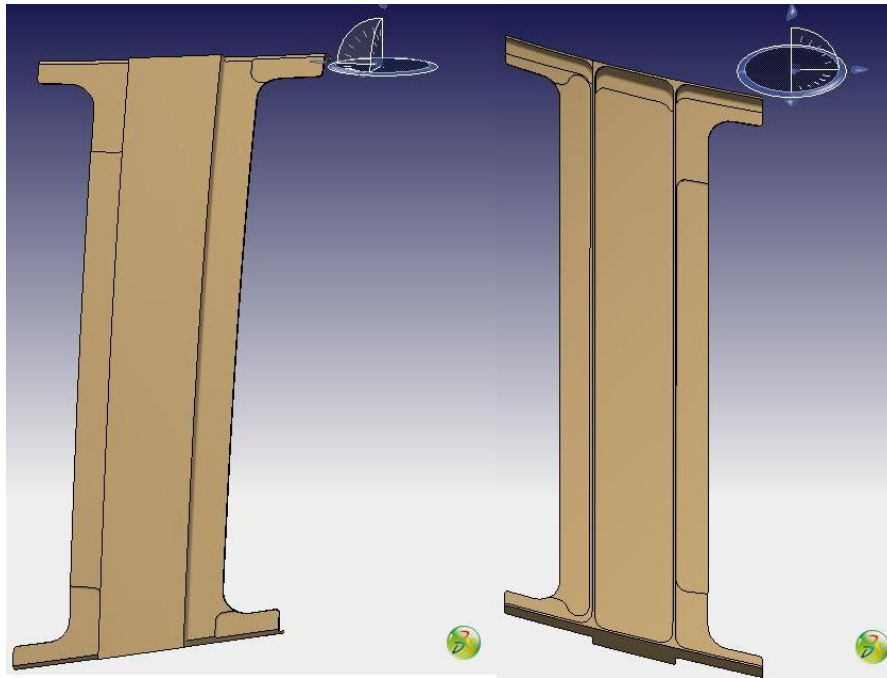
Proposta de alteração da viga lateral posterior da estrutura.
